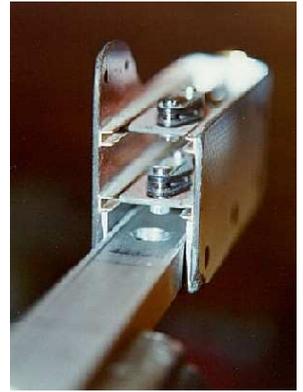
Die mittig in der Kopfplatte angebrachte Bohrung für die Spindel sitzt auf der gleichen Ebene wie die Führungsschienen.
